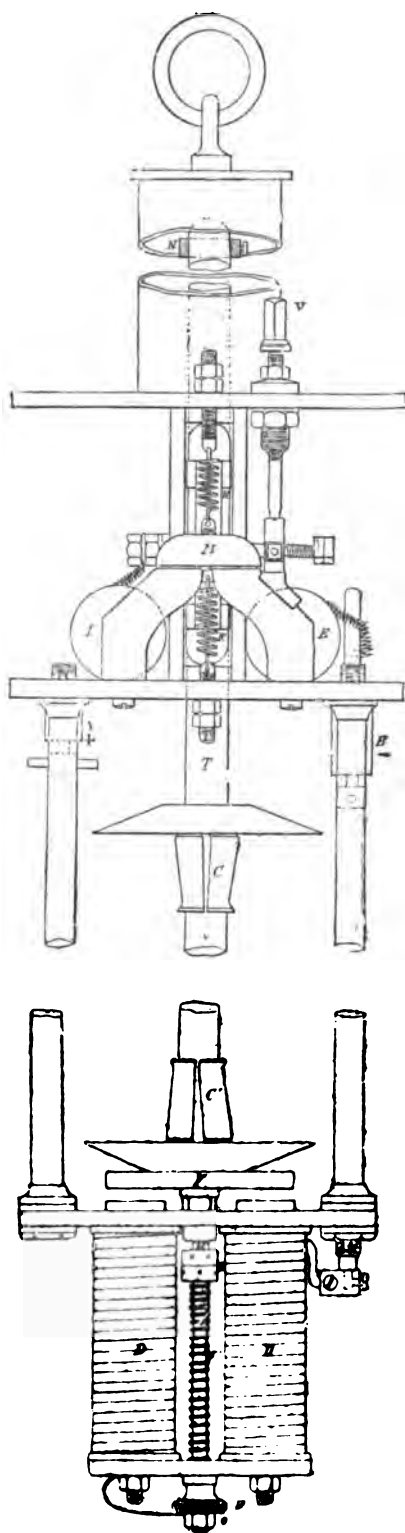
Régulateur Pieper à point lumineux mobile.
